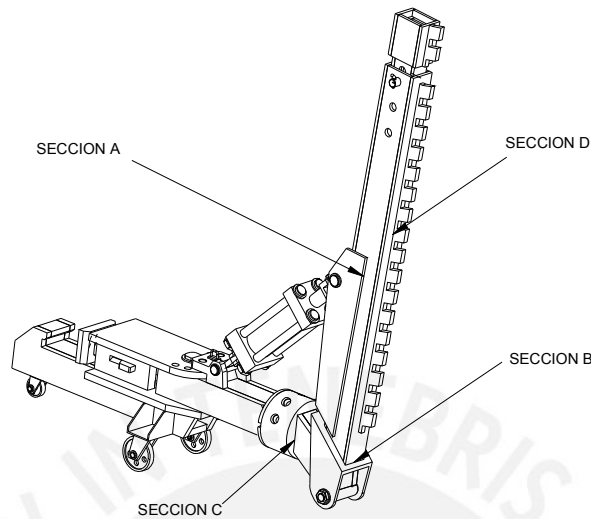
SECCIONES CRITICAS DE SOLDADURA
